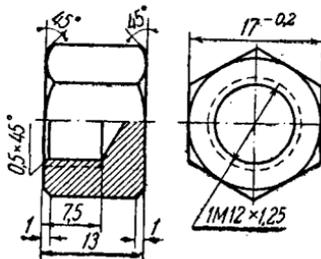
Дет. № 16-05. Гайка на корпус фильтра горячего
